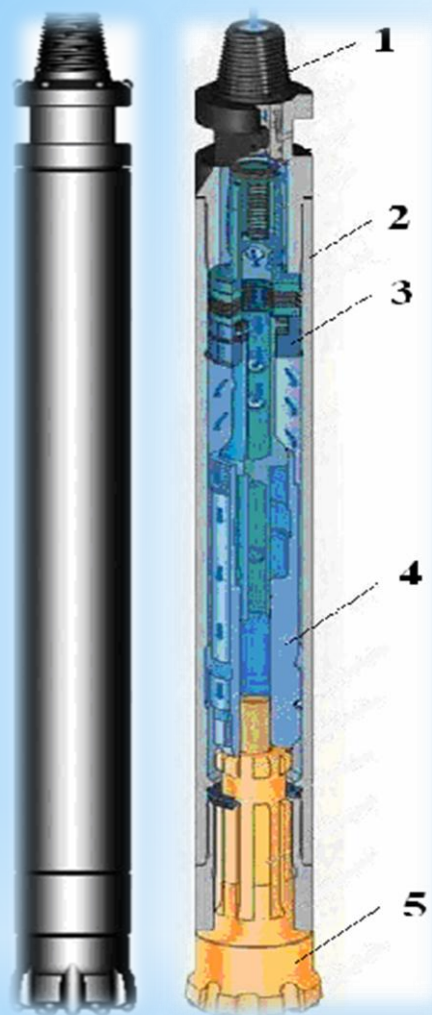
Загальний вигляд (а) і конструкція заглибного пневмоударника “Atlas Copco”(б): 1 - вузол з’єднаний з буровою штангою; 2 - корпус; 3 - золотниково-розподільчий механізм; 4 - ударний поршень; 5 - породоруйнівна коронка
